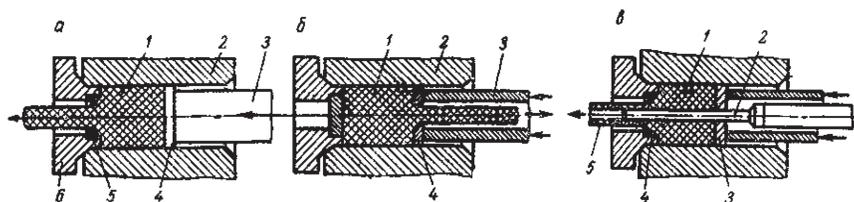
Прессование: а – прямое (1 – заготовка; 2 – контейнер; 3 – шплингот; 4 – пресс-шайба; 5 – матрица; 6 – матрицедержатель); б – обратное (1 – заготовка; 2 – контейнер; 3 – пуансон; 4 – матрица); в – прямое прессование труб (1 – заготовка; 2 – игла; 3 – пресс-шайба; 4 – матрица; 5 – труба)
